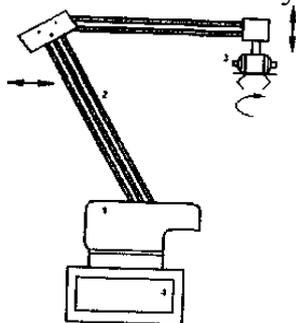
Схема манипулятора: 1 - силовой привод; 2 рычажный механизм; 3 - грузовой блок; 4 – кронштейн
